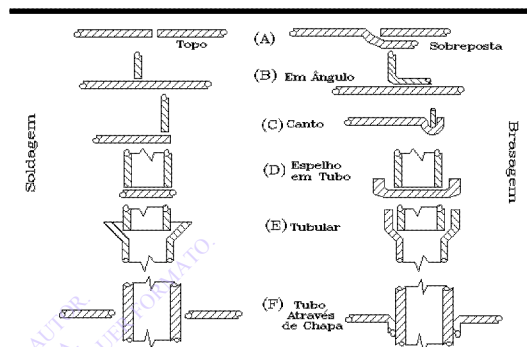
Juntas para Soldagem e Brasagem (à direita).
